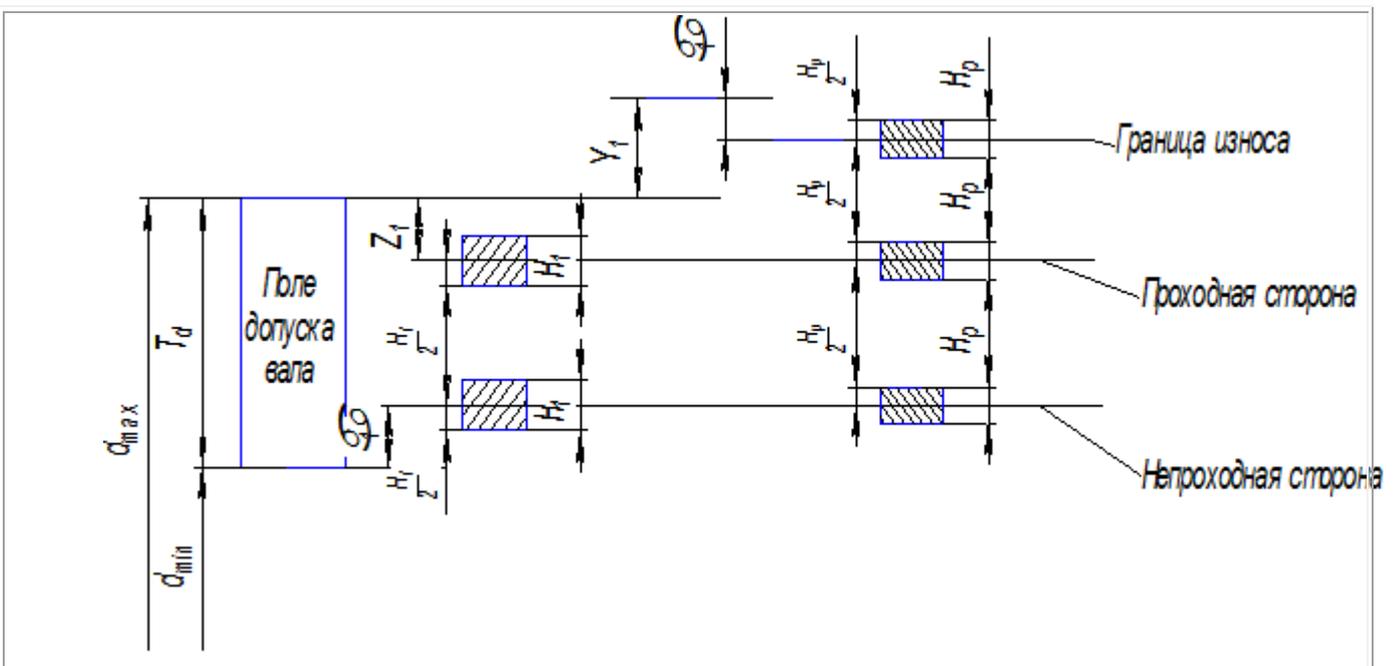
Схема расположения полей допусков калибров для контроля валов и кондукторных калибров
